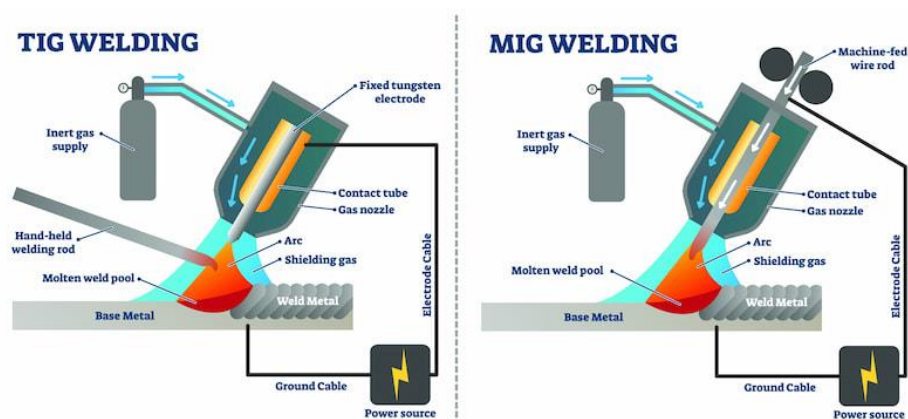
Diferencias entre la soldadura TIG y MIG
